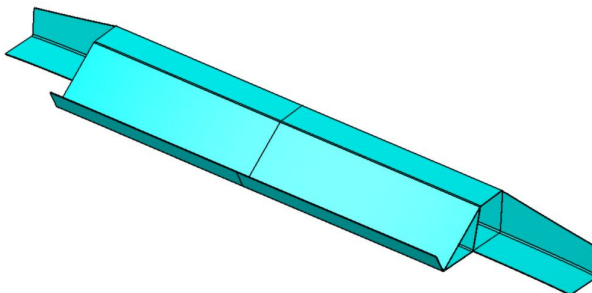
, 98: Spojka profil C sloupek – zadní profil levá
